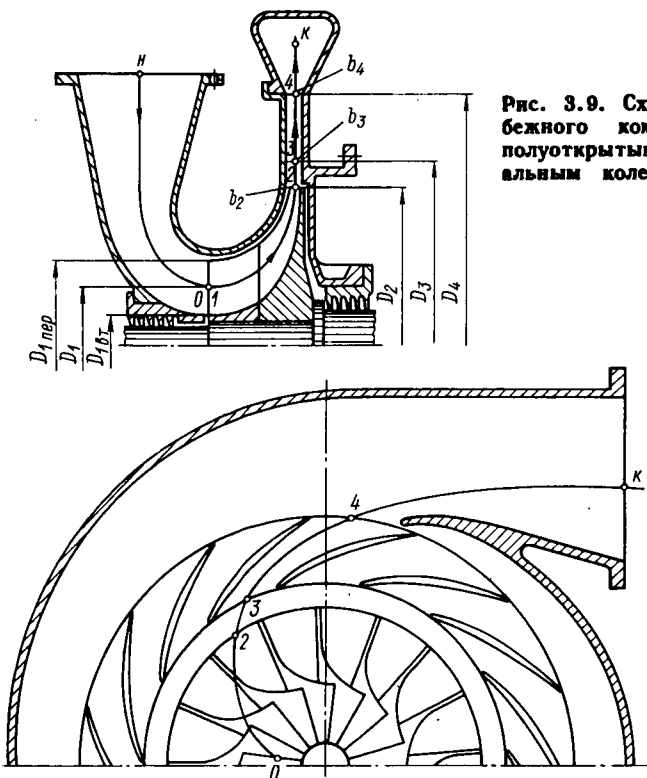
Схема центробежного компрессора с полукрытым осерadiальным колесом
